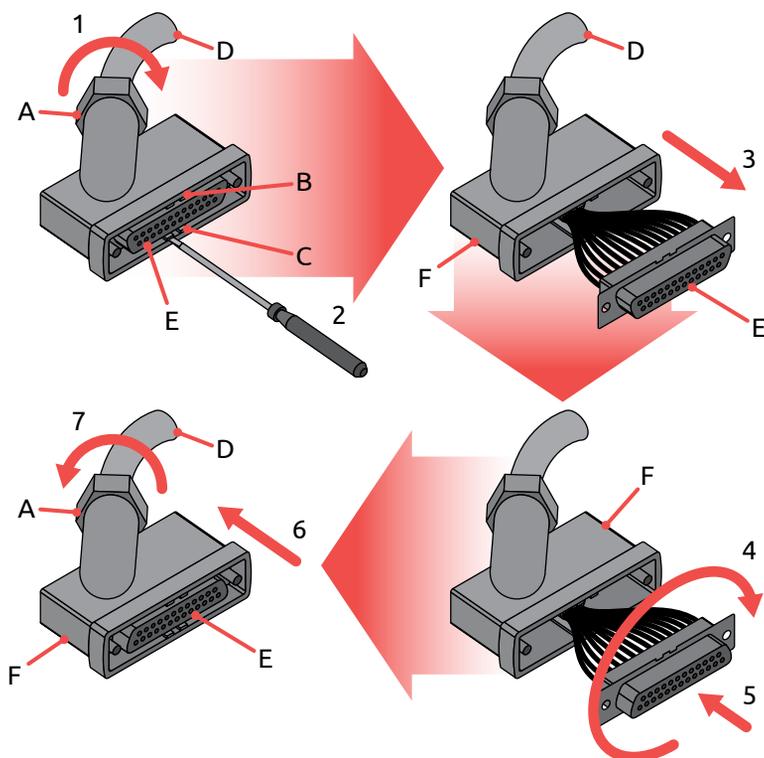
Разворот корпуса разъема кабеля VPI-ZCN-S25-xx
